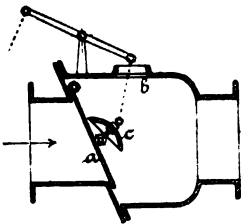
Rückschlagventil für Gebläsewindleitungen.
